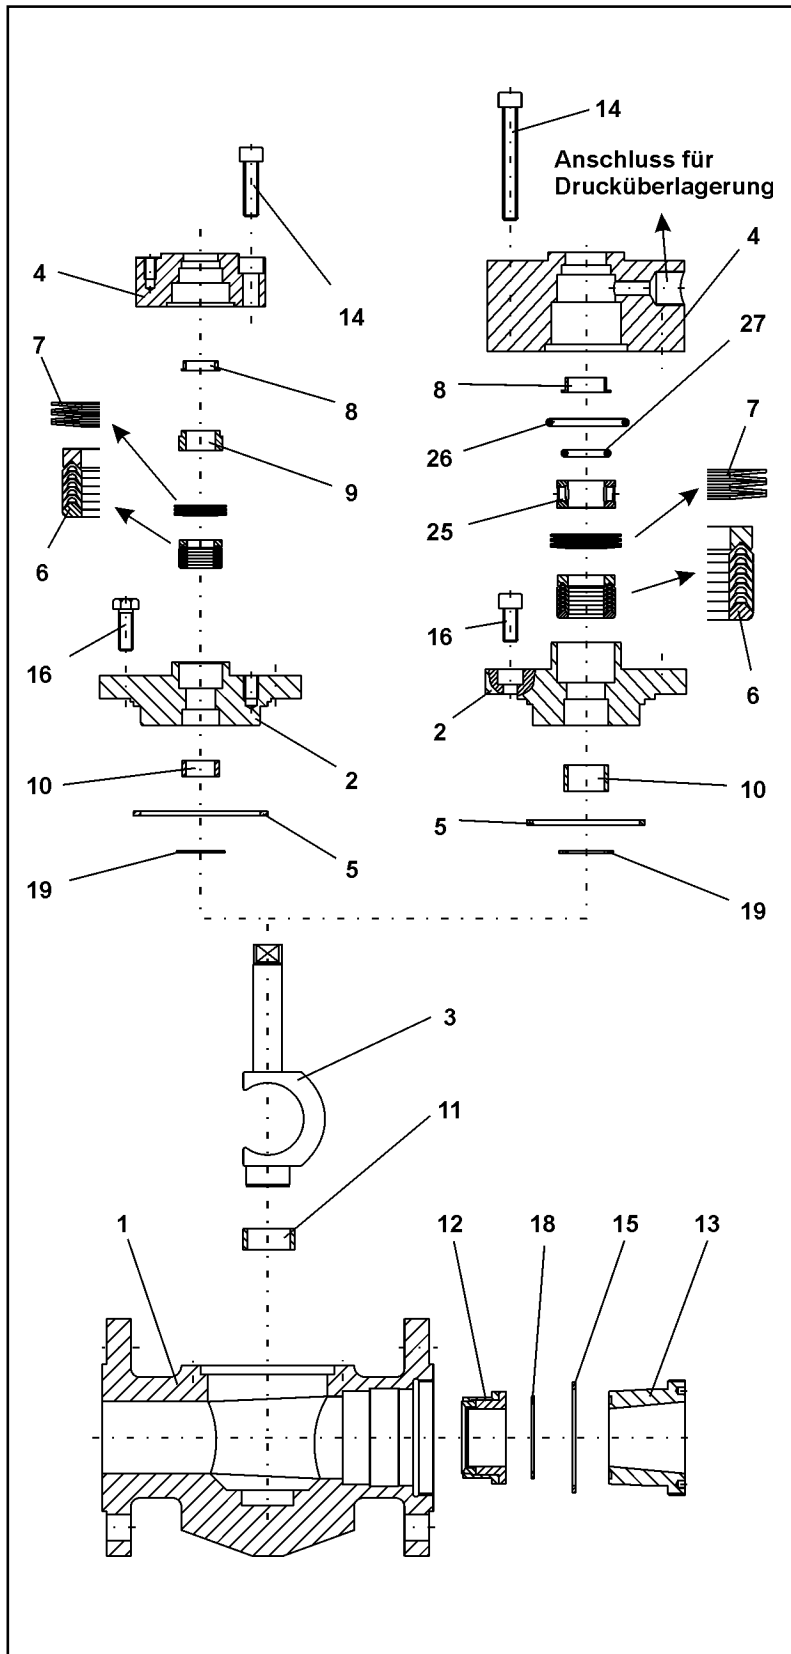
Explosionszeichnung des Drehkegelventils BR 23b
